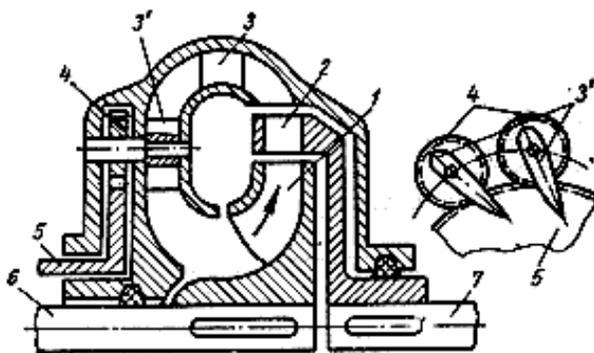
Схема одноступенчатого регулируемого ГДТ «Фойт» с поворотными лопатками реактора
